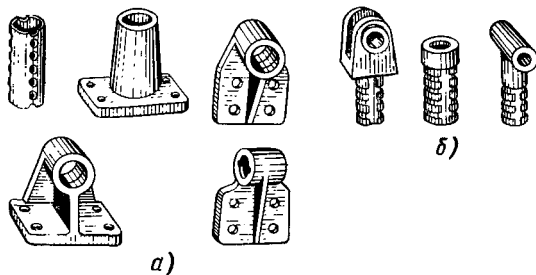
Типовые конструкции установочных элементов сборочных приспособлений:
